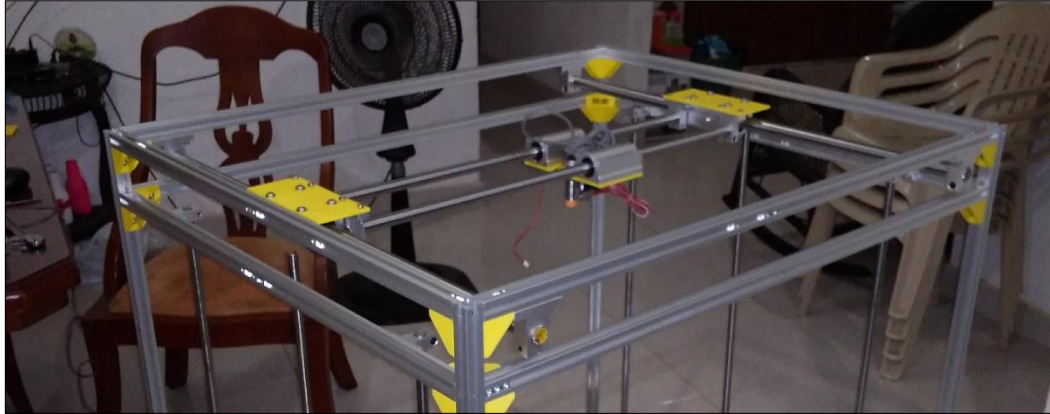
Montaje sistema CoreXY. Fuente: Autor, 2017
